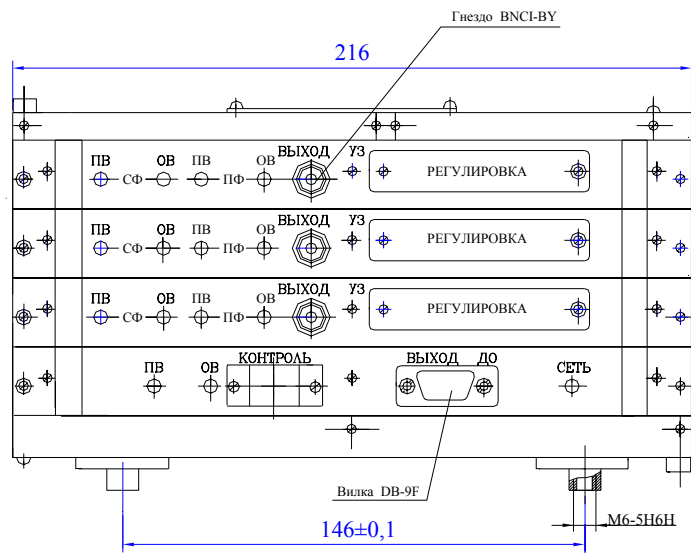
Габаритно-установочные размеры блока БЭ-38-6М.1-АИ
